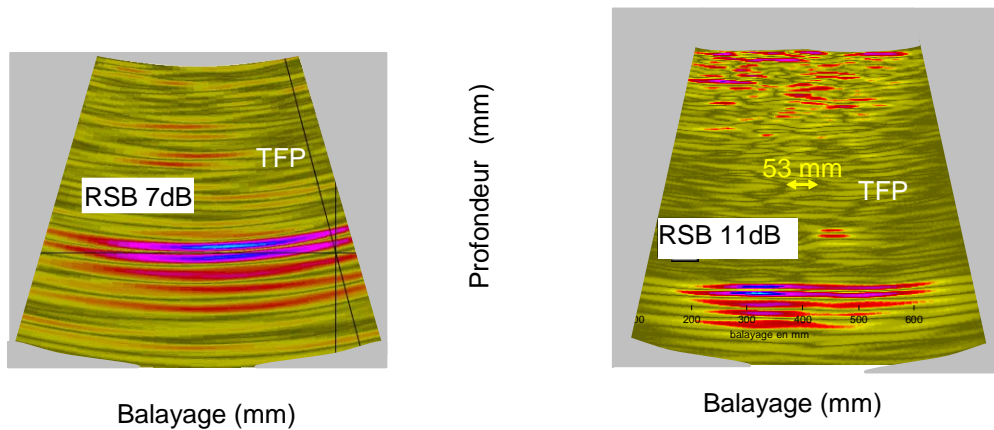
a) Bscan angulaire reconstruit montrant l'écho du trou à fond plat b) Bscan 'global' reconstruit
